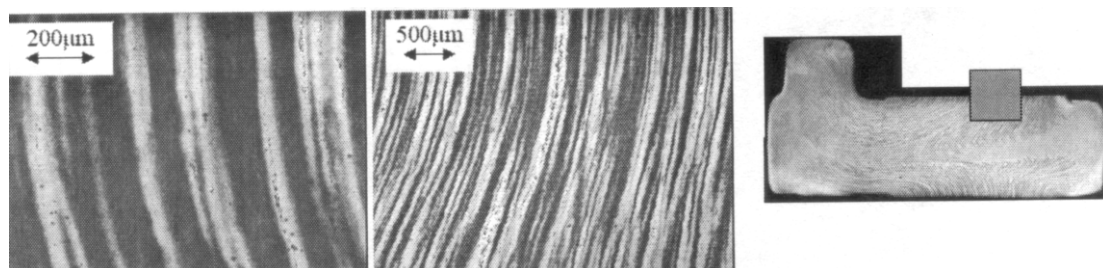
Agrandissement de la zone type forgeage classique d'une macrographie de la pièce SKL thixoforgée ; attaque Le Chatelier.
